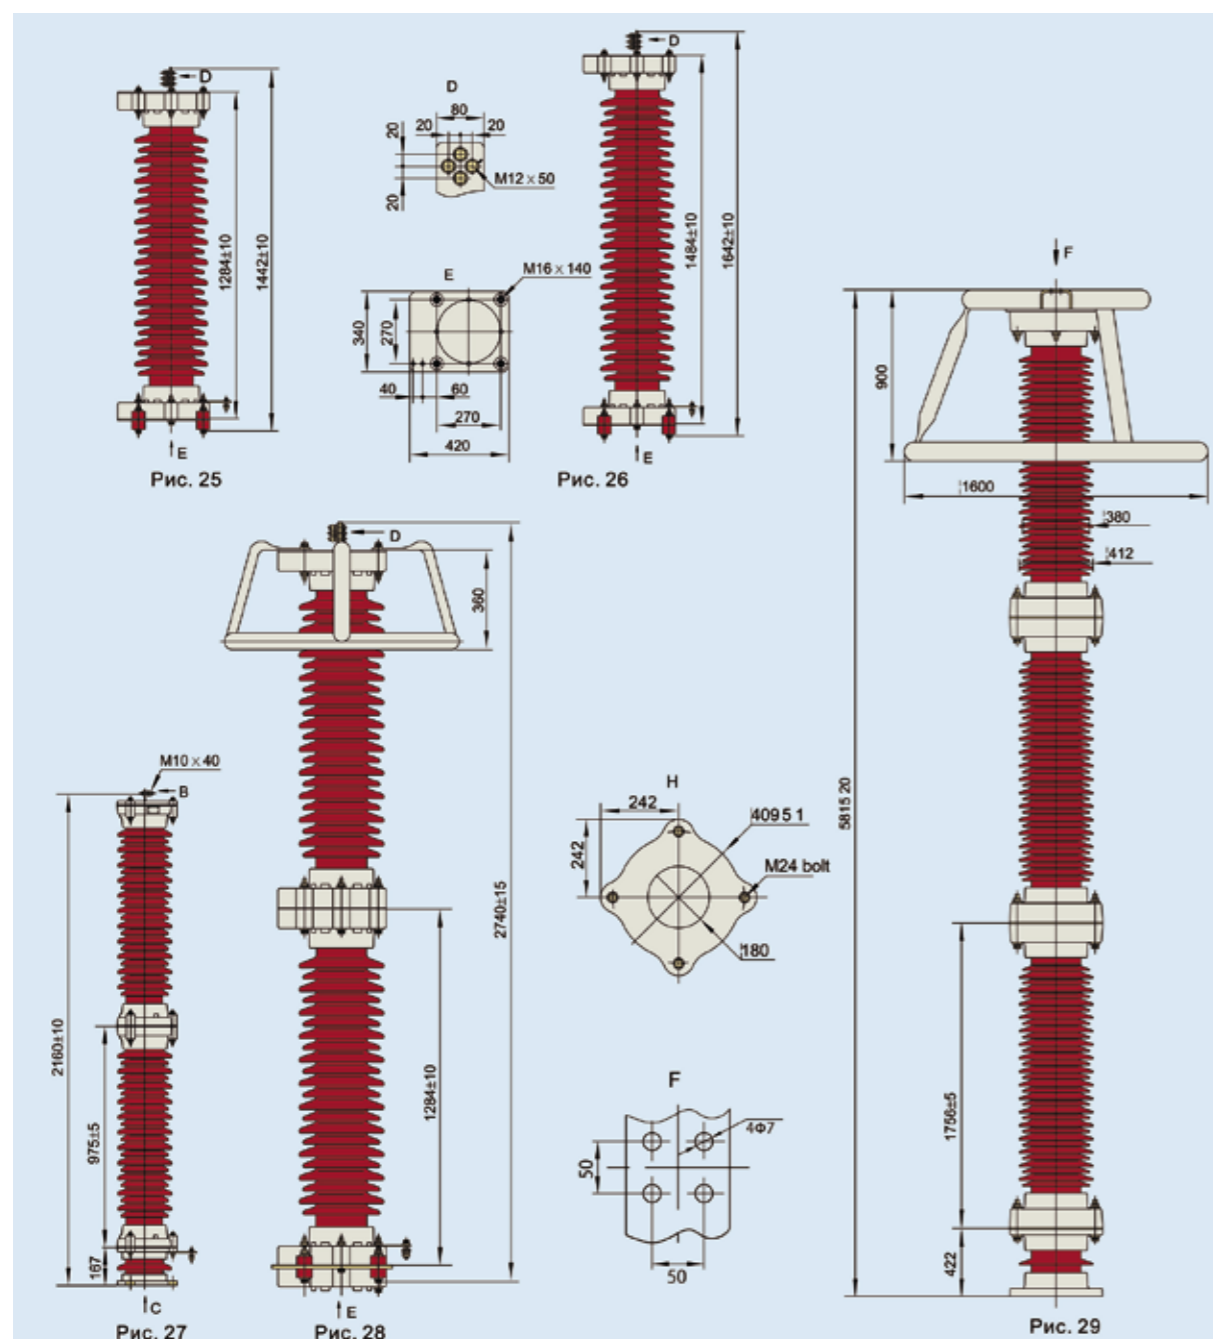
Внешний вид и размеры металлооксидного ОПН
